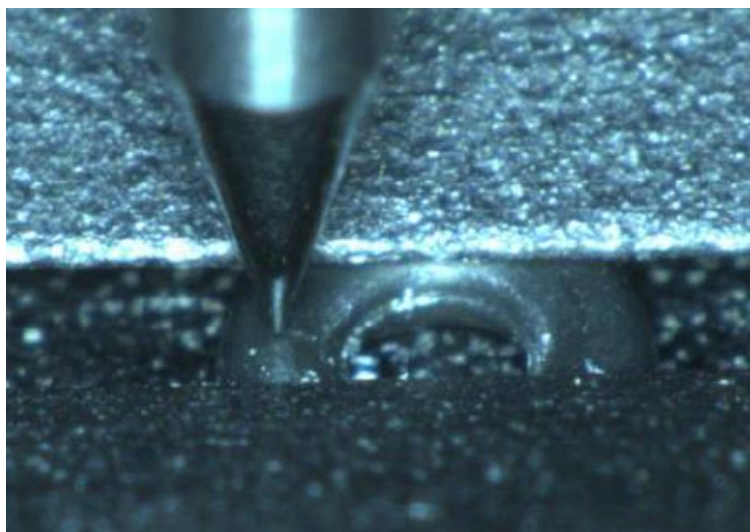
Härtemessung eines O-Ringes mit einem Durchmesser von 0,5 mm mit Hilfe des LNP® nano touch (Bild: O-Ring Prüflabor Richter)
